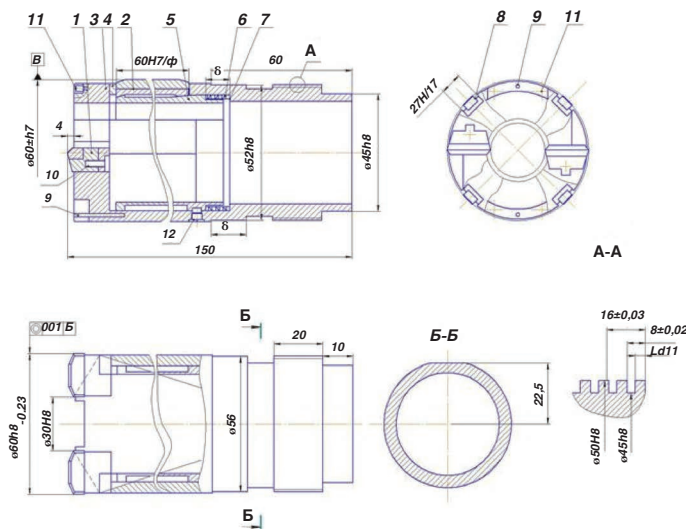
Сверлильная головка диаметром 60 мм: 1 — резцовый блок; 2 — направляющая колодка; 3 — планшайба резцовая; 4 — корпус; 5 — клин; 6 — пружина втулочно-прорезная; 7 — шайба; 8 — кольцо разрезное; 9 — штифт; 10 — винт; 11 — винт; 12 — винт, фиксирующий угловое положение клина.
